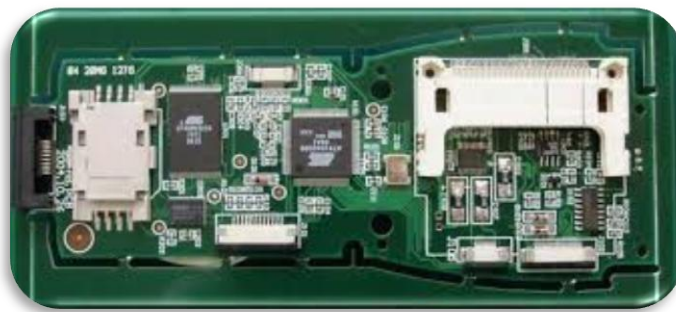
PCB. (Printed Circuit Board) Tarjeta de Circuito Impreso
